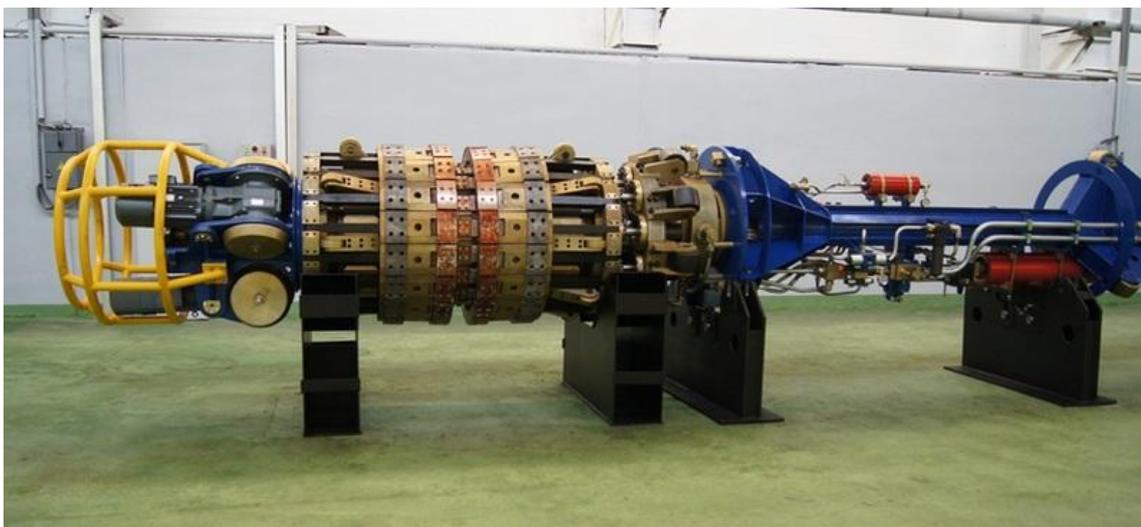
комплекс для контактной стыковой сварки труб с Ду 530 мм
